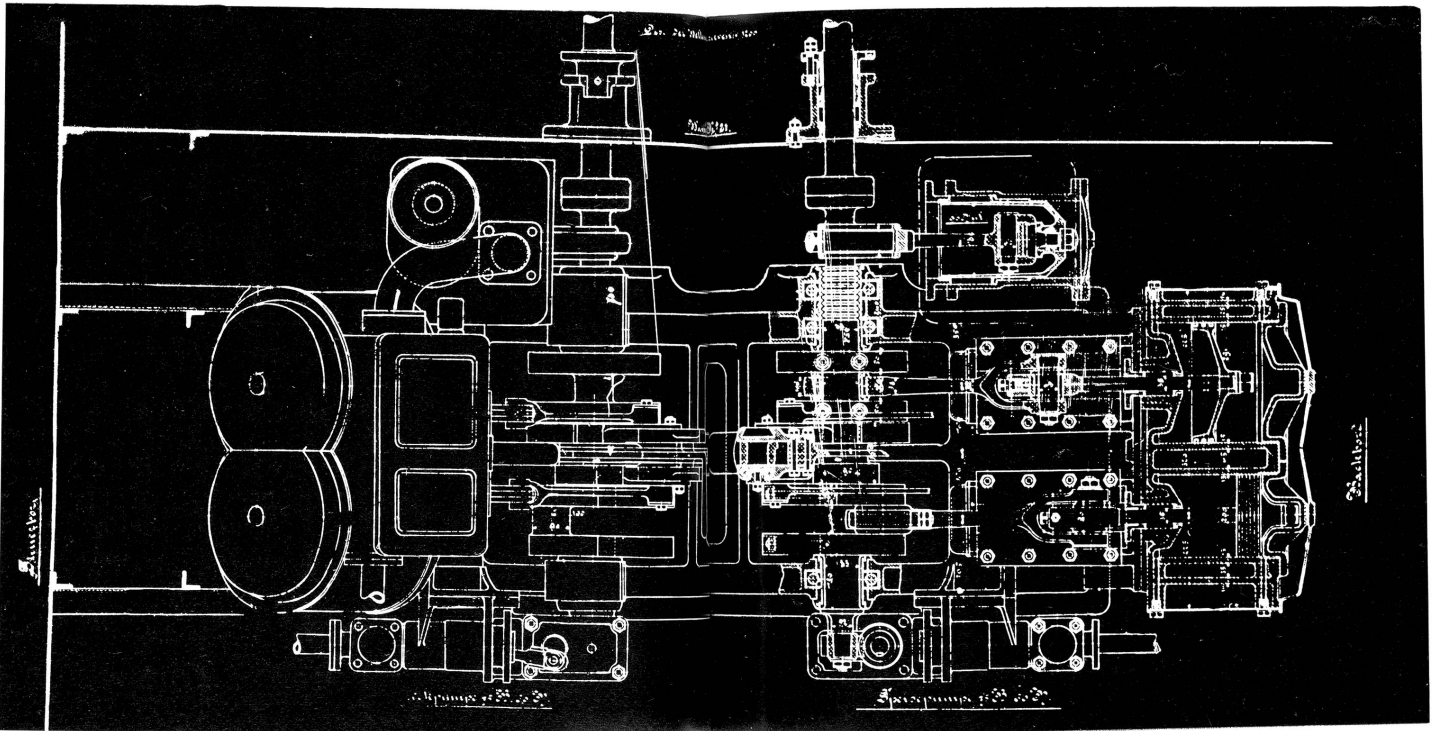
Maschinenanlage. Grundriss. Von vorn gesehen.
